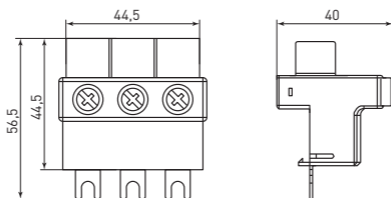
Габаритные размеры соединительного блока АПД/GV2
